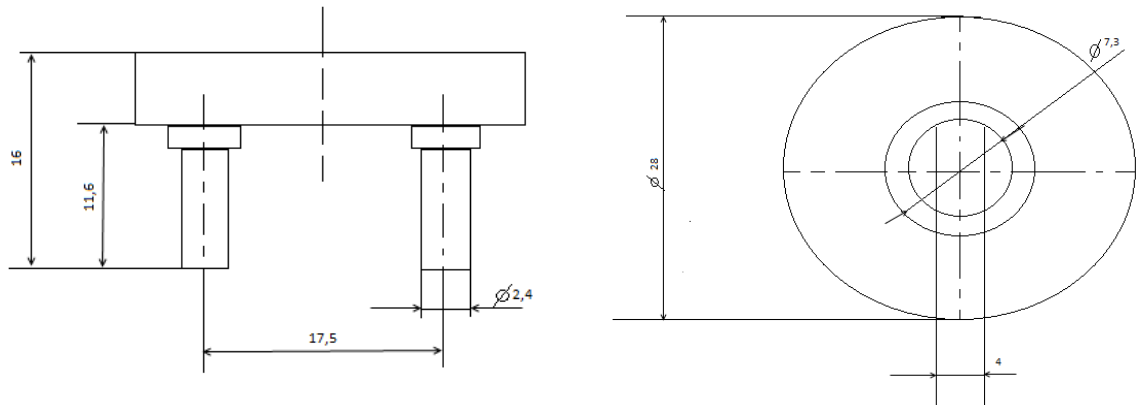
Цоколевка и размеры фоторезистора ФСК-1
